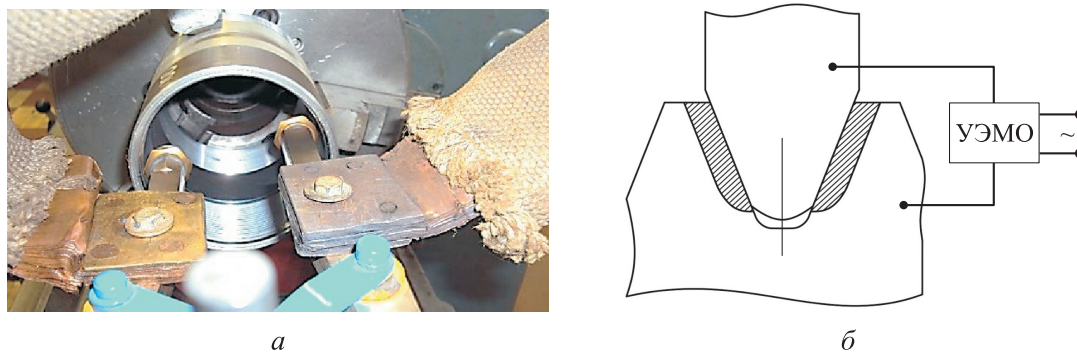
Внешний вид (а) и схема упрочнения (б) резьбы корпуса ЭМО
